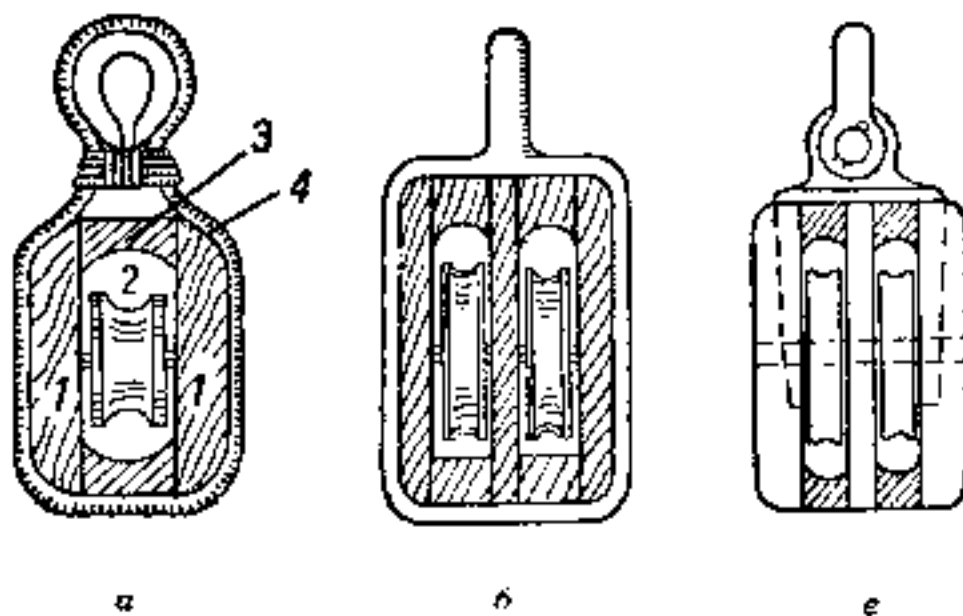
Деревянные блоки: а — одношкивный блок: 1 — щеки; 2 — шкив; 3 — вкладыши; 4 — строп; б — двухшкивный блок с наружной оковкой; в — деревянный двухшкивный блок с внутренней оковкой
